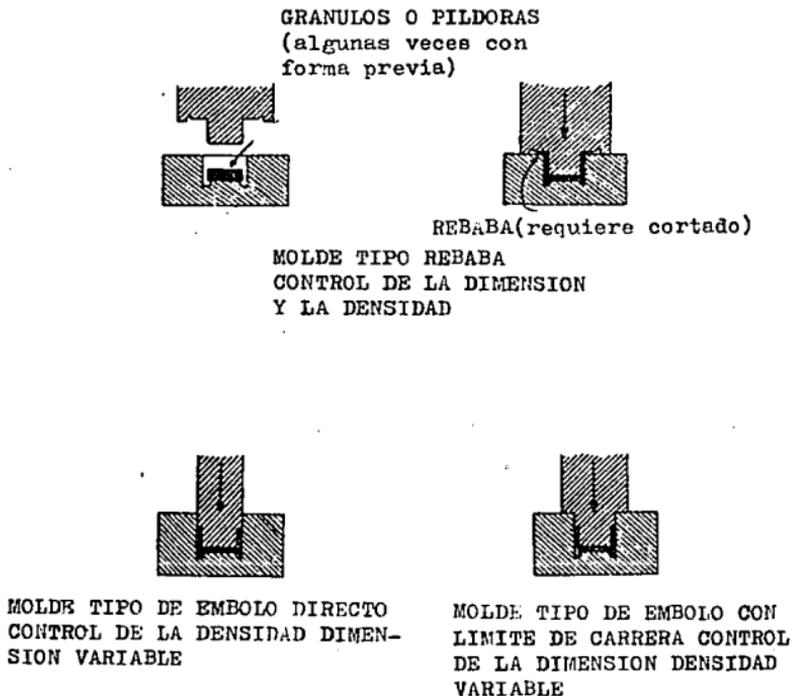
TIPOS DE MOLDES POR COMPRESION
